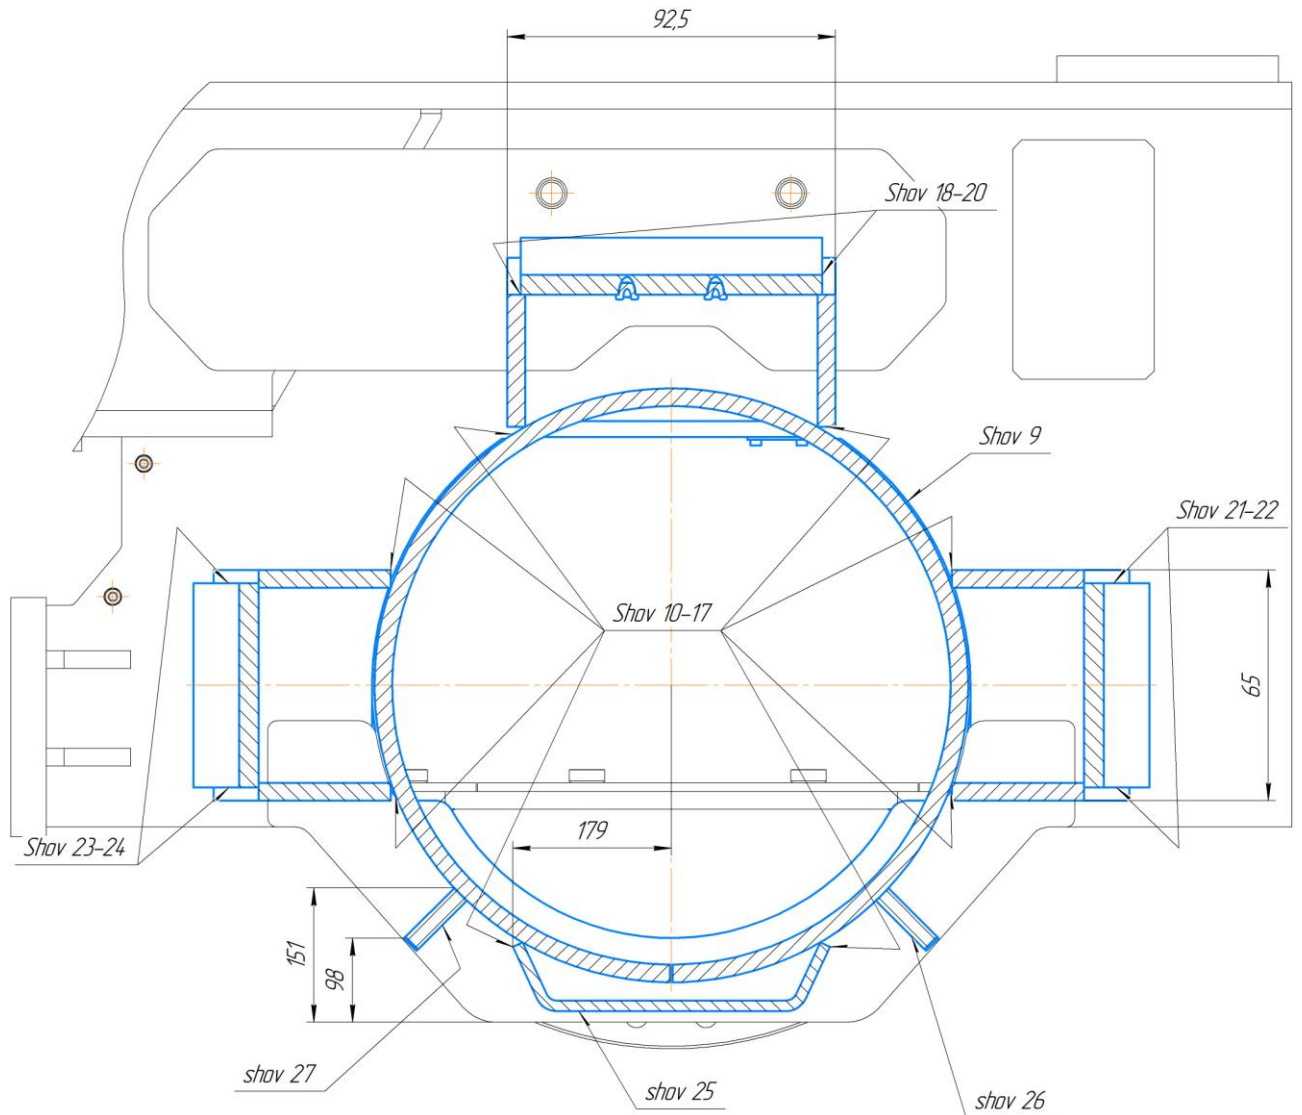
Корпус бортовых редукторов трубоукладчика
